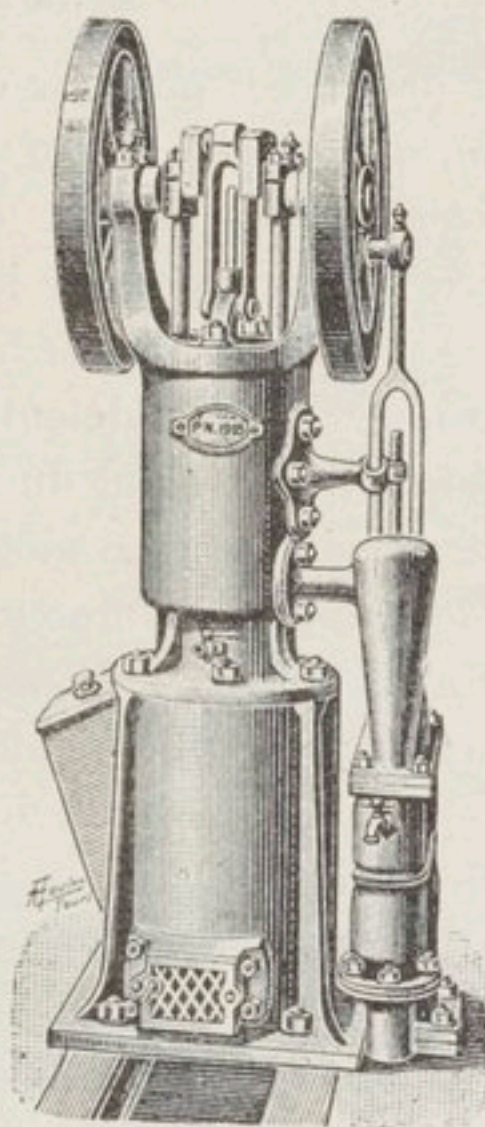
Moto-pompe à air chaud Noël. Vue d'ensemble.
